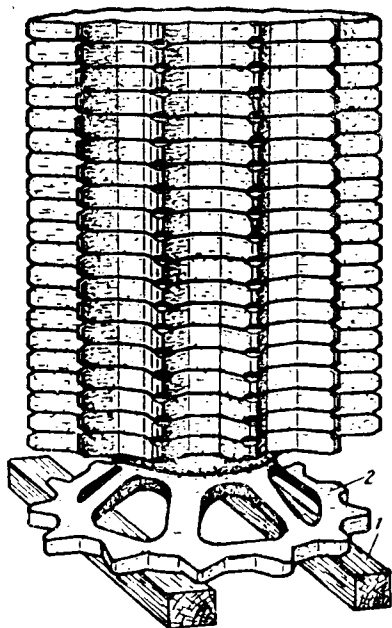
Пакет ведущих колес трактора ДТ-75:
